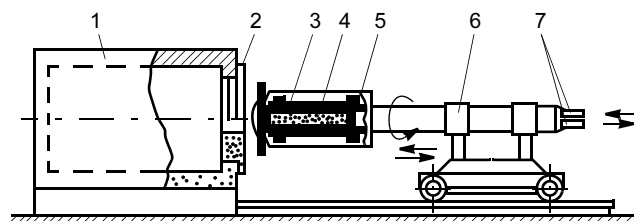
Комплекс устройств для пайки решетчатых крыльев: 1 — высокотемпературная печь; 2 — разъемная дверца; 3 — фиксирующее приспособление; 4 — паяемое изделие; 5 — контейнер; 6 — тележка-манипулятор; 7 — трубопроводы два циркуляции газовой среды
